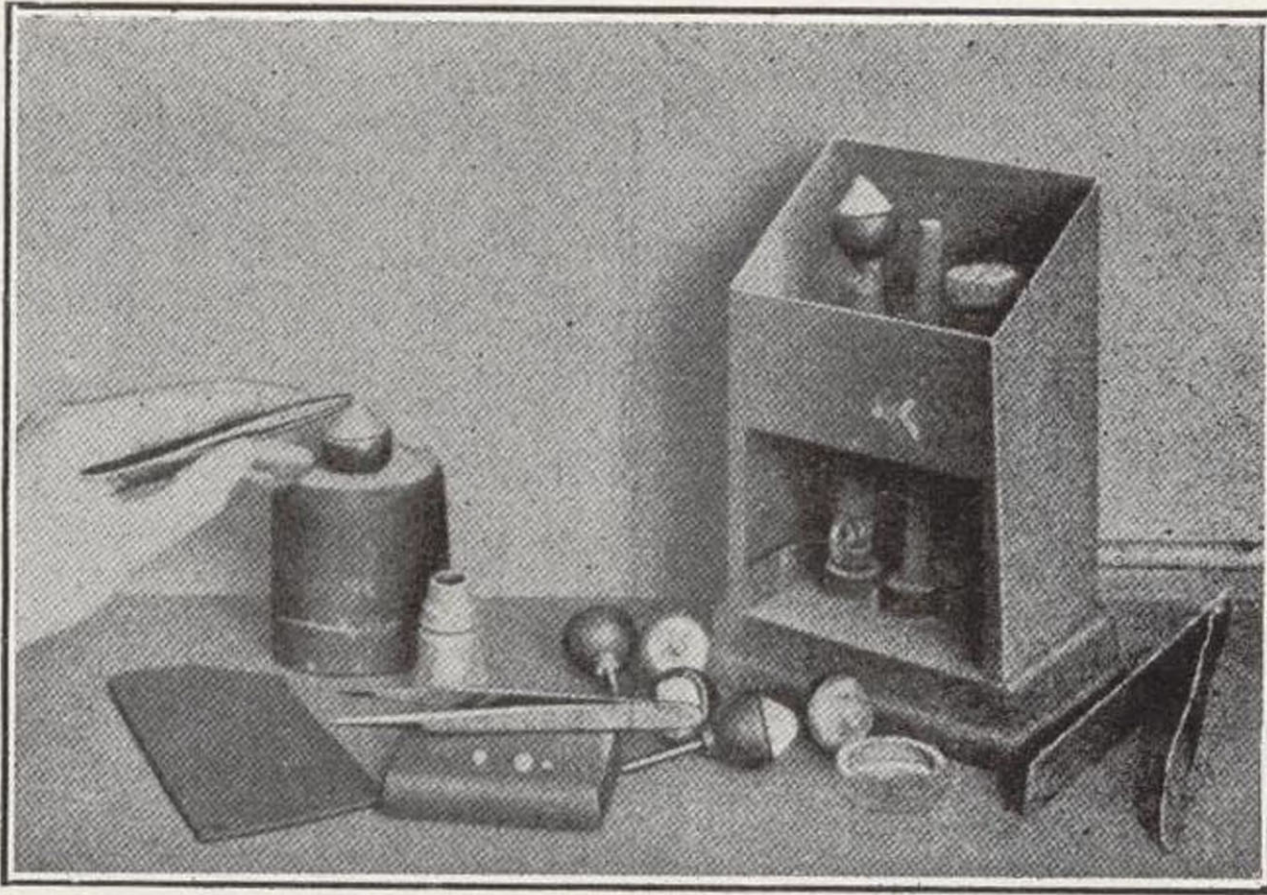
Soldadura de los diamantes, al soporte, con estaño
